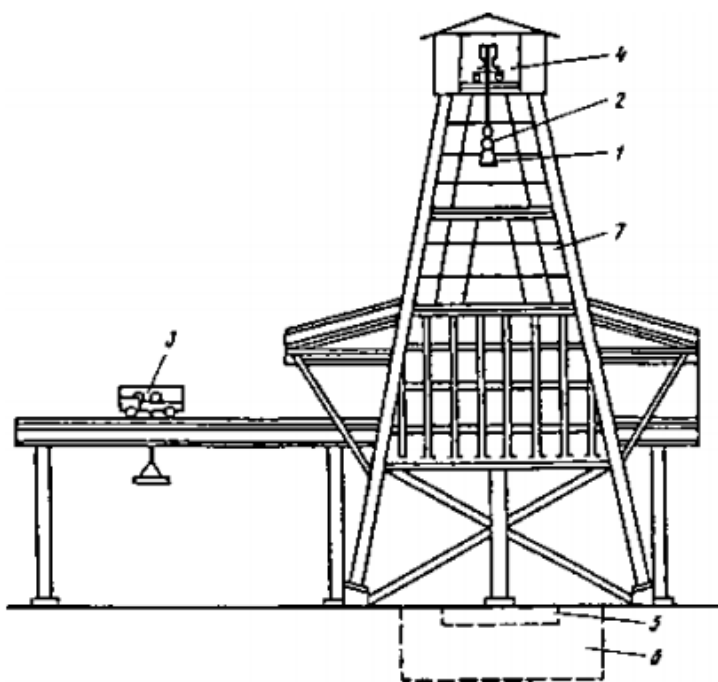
Баштовий копер для подрібнення металевого брухту:
